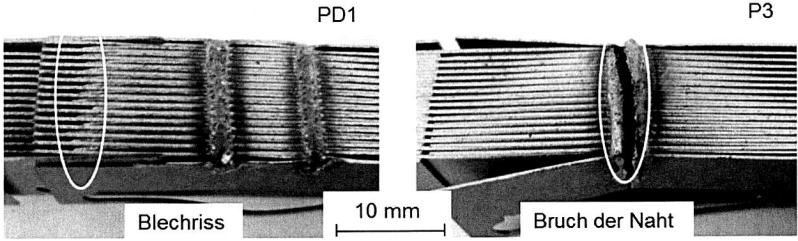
Schadensmechanismen der geschweißten Zugproben des Werkstoffes M330-35A an ausgewählten Parameterkombinationen.
